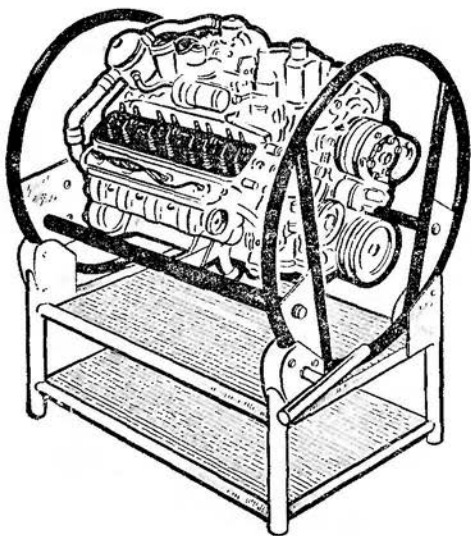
Поворотный стенд для разборки и сборки двигателя
